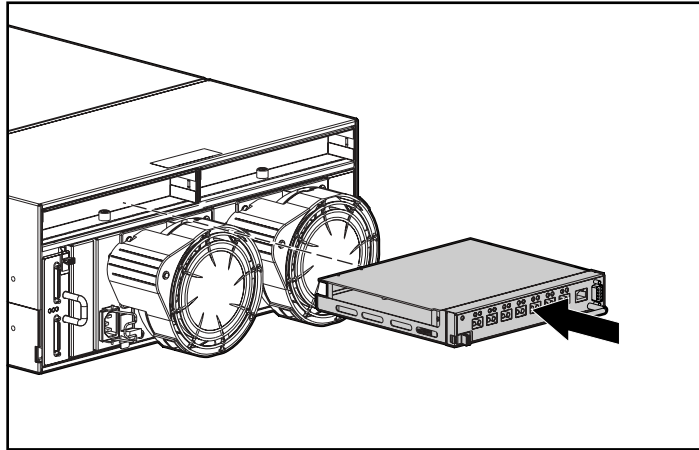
Einbauen des MSA SAN Switch 2/8
